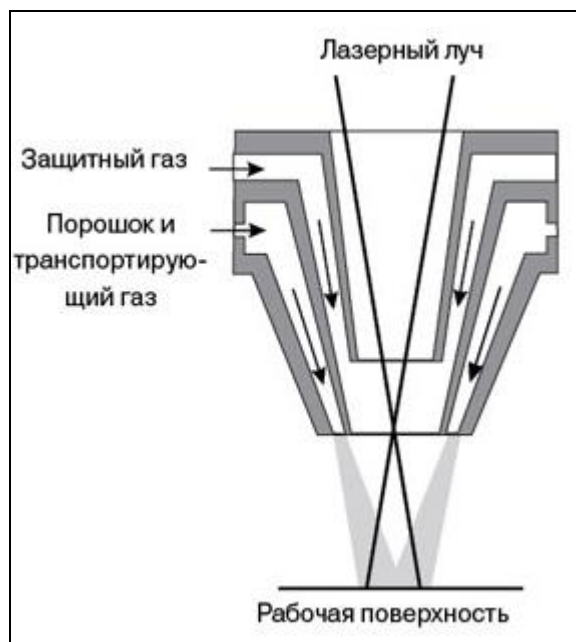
Схема наплавки с коаксиальной подачей порошка.
